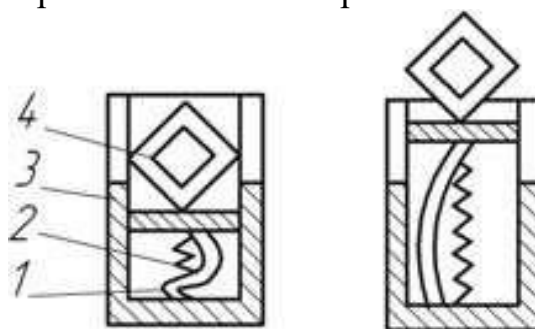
Схема устройства для выдвижения рамки из корпуса
